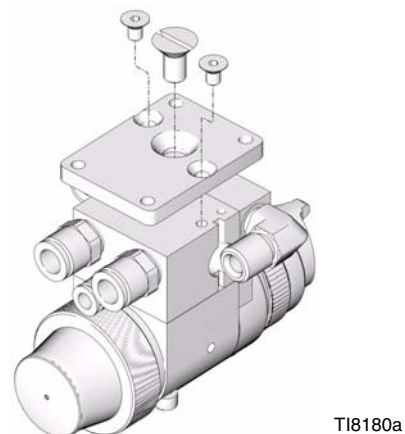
Montaje con placa adaptadora para retroinstalaciones
